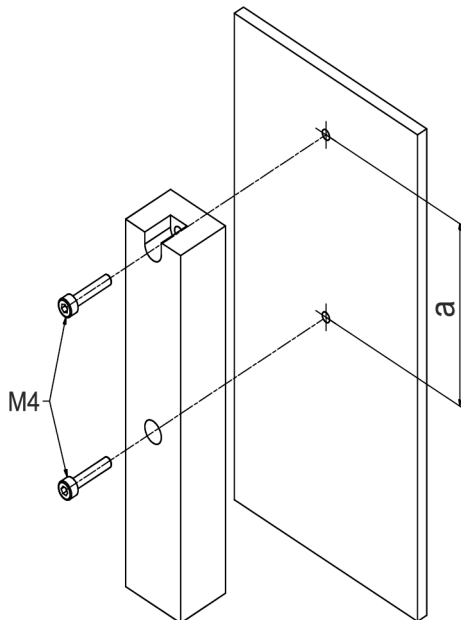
Montage mit zwei Befestigungsschrauben M4
